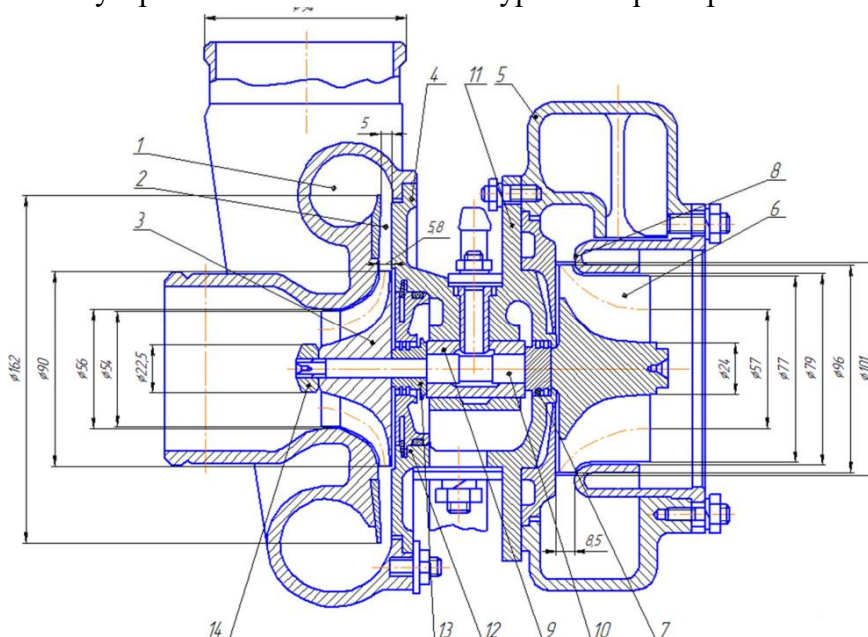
Устройство автомобильного радиального турбокомпрессора ТКР-90-2: 1 – улитка; 2 – диффузор безлопаточный; 3 – колесо компрессора; 4 – крышка корпуса компрессора; 5 – корпус турбины; 6 – колесо турбины; 7 – кольцо упорное; 8 – аппарат силовой; 9 – моноштулка; 10 – вал ротора; 11 – крышка корпуса турбины; 12 – кольцо уплотнительное; 13 – маслоотражатель; 14 – гайка крепления колеса компрессора
